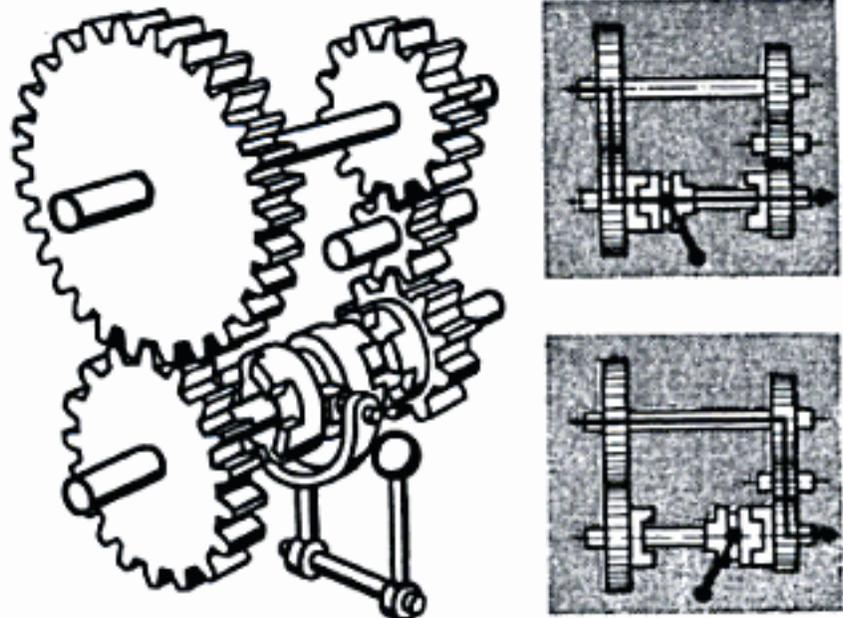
,1 Mecanismo de inversión de ruedas dentadas rectas o frontales
